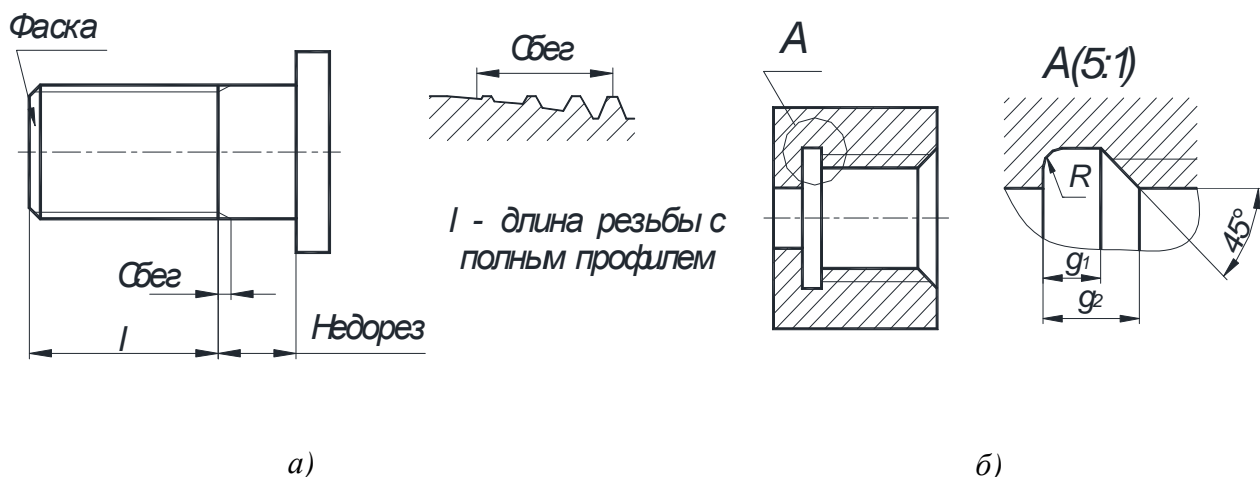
Изображение сбega (а) и проточки (б) резьбы
